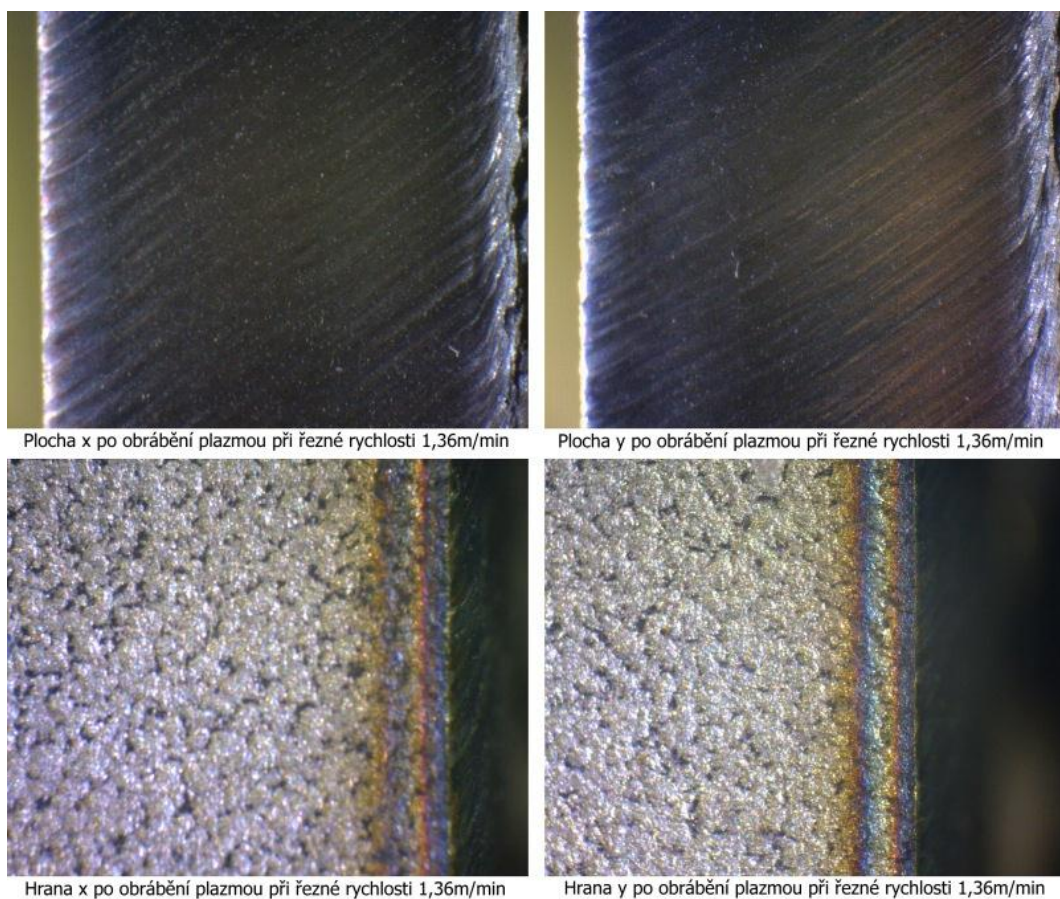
Snímky z mikroskopu vzorku 3 obráběného plazmou - materiál 17 349
